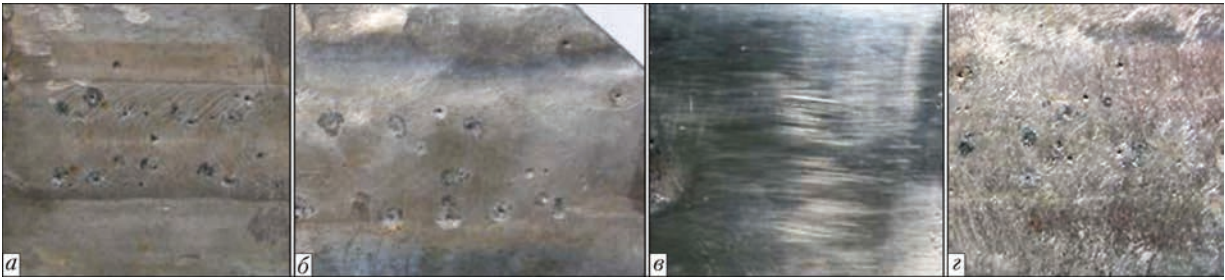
Поверхность сварных соединений шлифованной нержавеющей стали, испытанных на питтинговую коррозию после сварки (а), проковки (б), полировки (в), торцевого трения (з)
